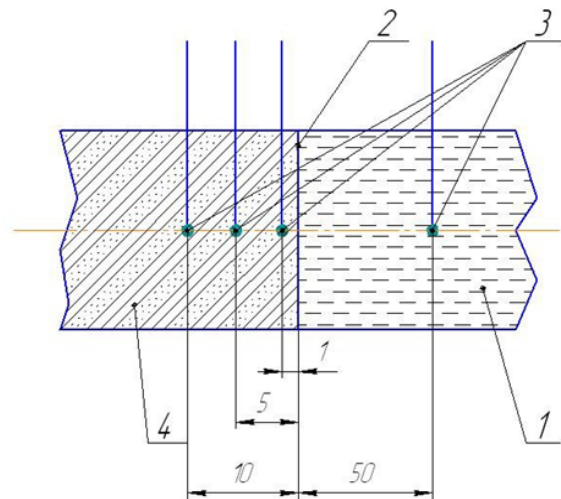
Схема розташування термопар: 1 — рідкий метал; 2 — межа розділу метал — форма; 3 — термопари; 4 — заморожена форма
